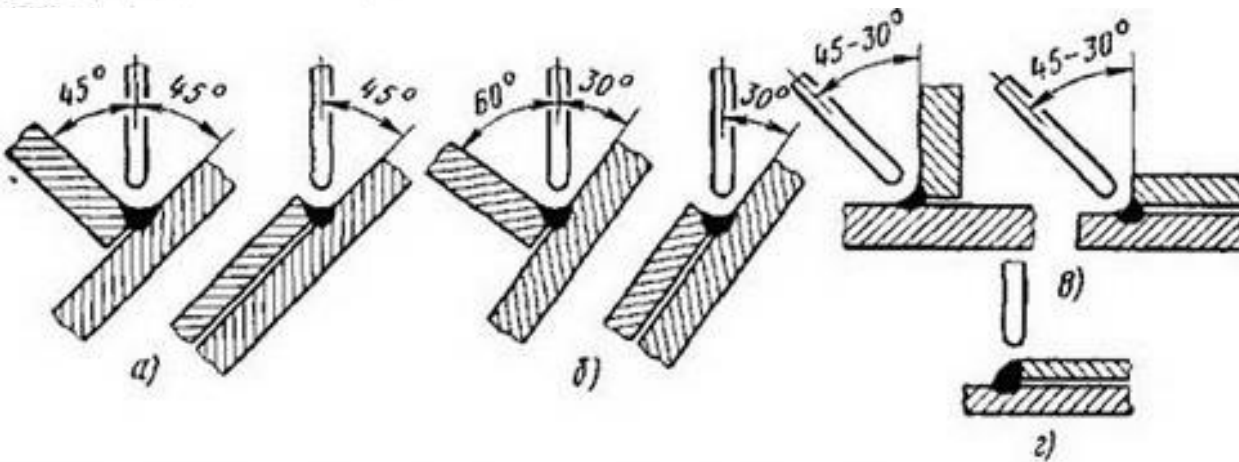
Различные методы сварки угловых швов:
